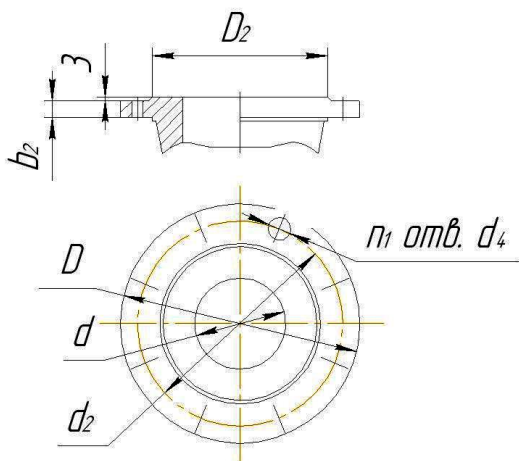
Габаритные и присоединительные размеры насосов типа «ХМ»
